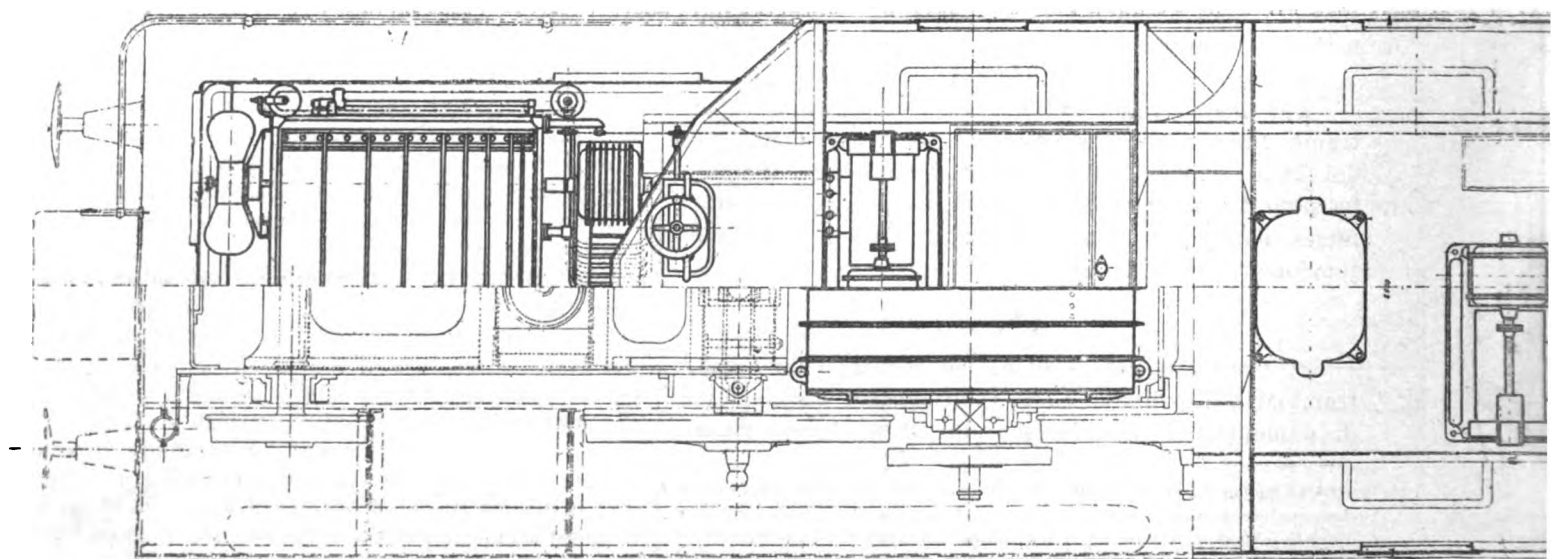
Pianta metà in vista e metà in sezione secondo un piano passante per la base della
